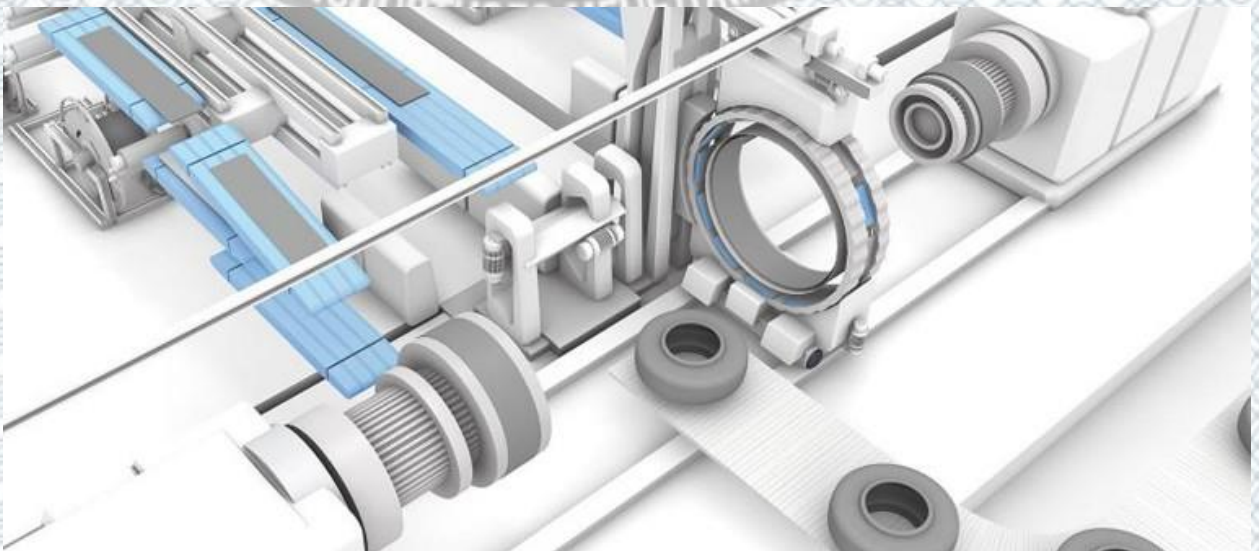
Загальний вигляд верстату для збірки шин
